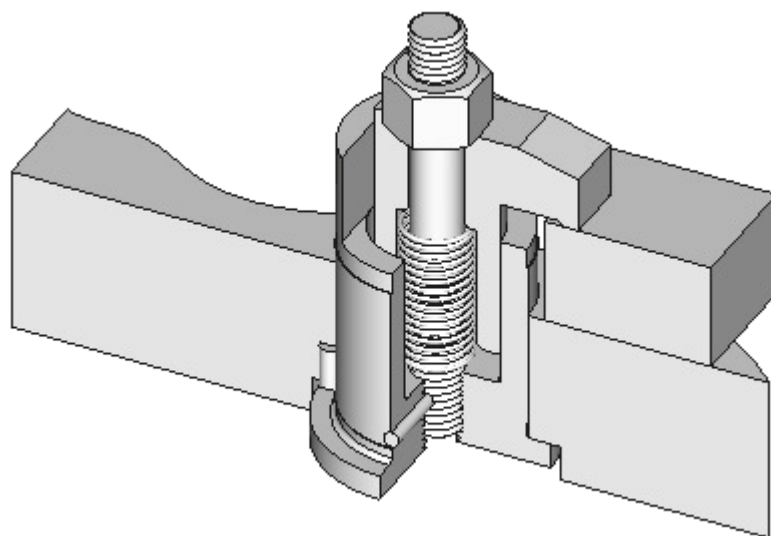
Прихват Г-образный в приспособлении с заготовкой
